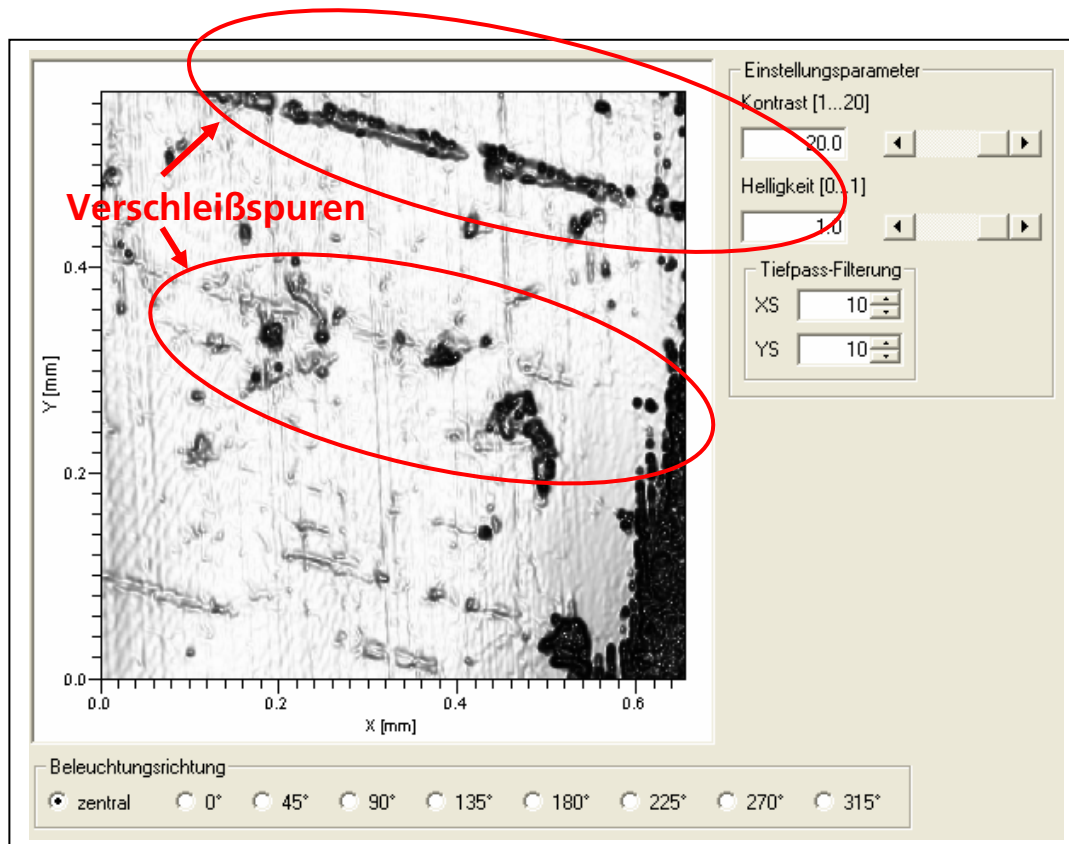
Aufnahme (Draufsicht) Zylinderwand Weißlichtinterferometer (künstlich beleuchtet)
